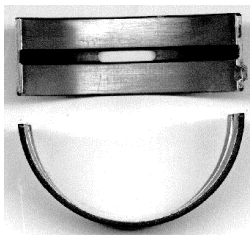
Коренной подшипник коленвала двигателя с заливкой баббитом
